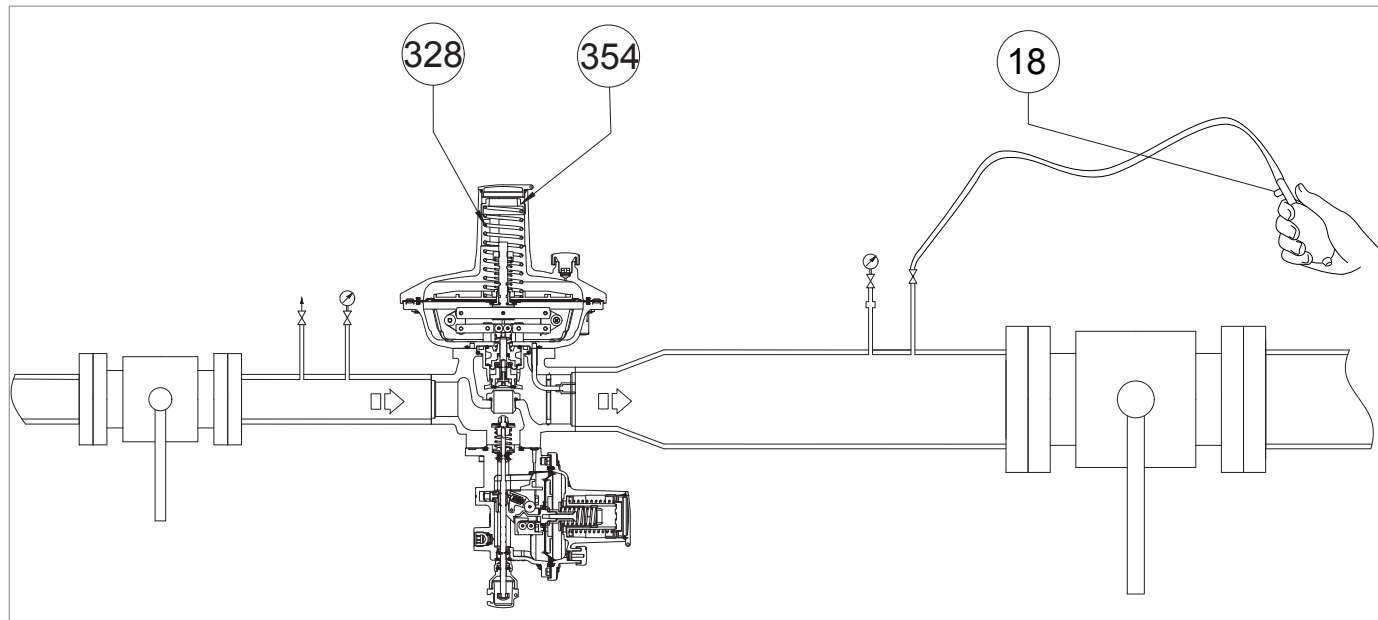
Druckbeaufschlagung mit externer Quelle für eingebautes Absperrventil LA
